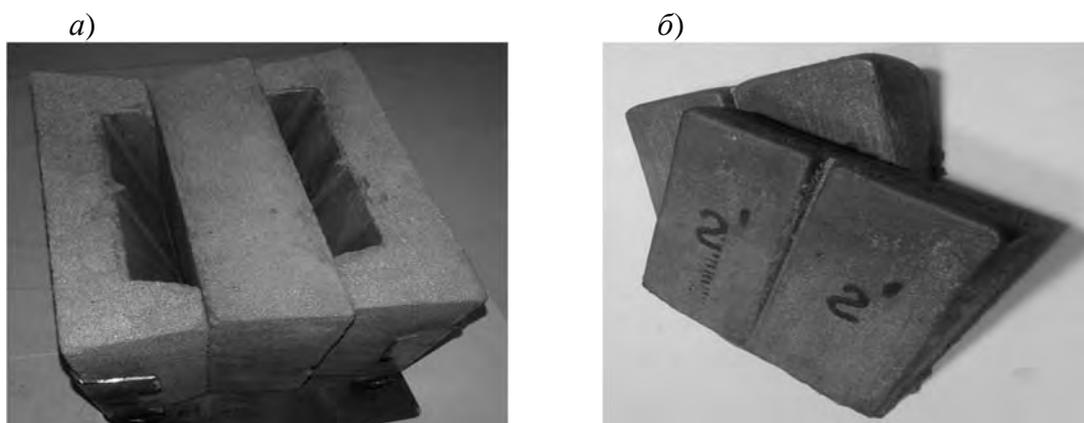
Форма в сборе (*а*) для заливки клиновидной пробы (*б*)
